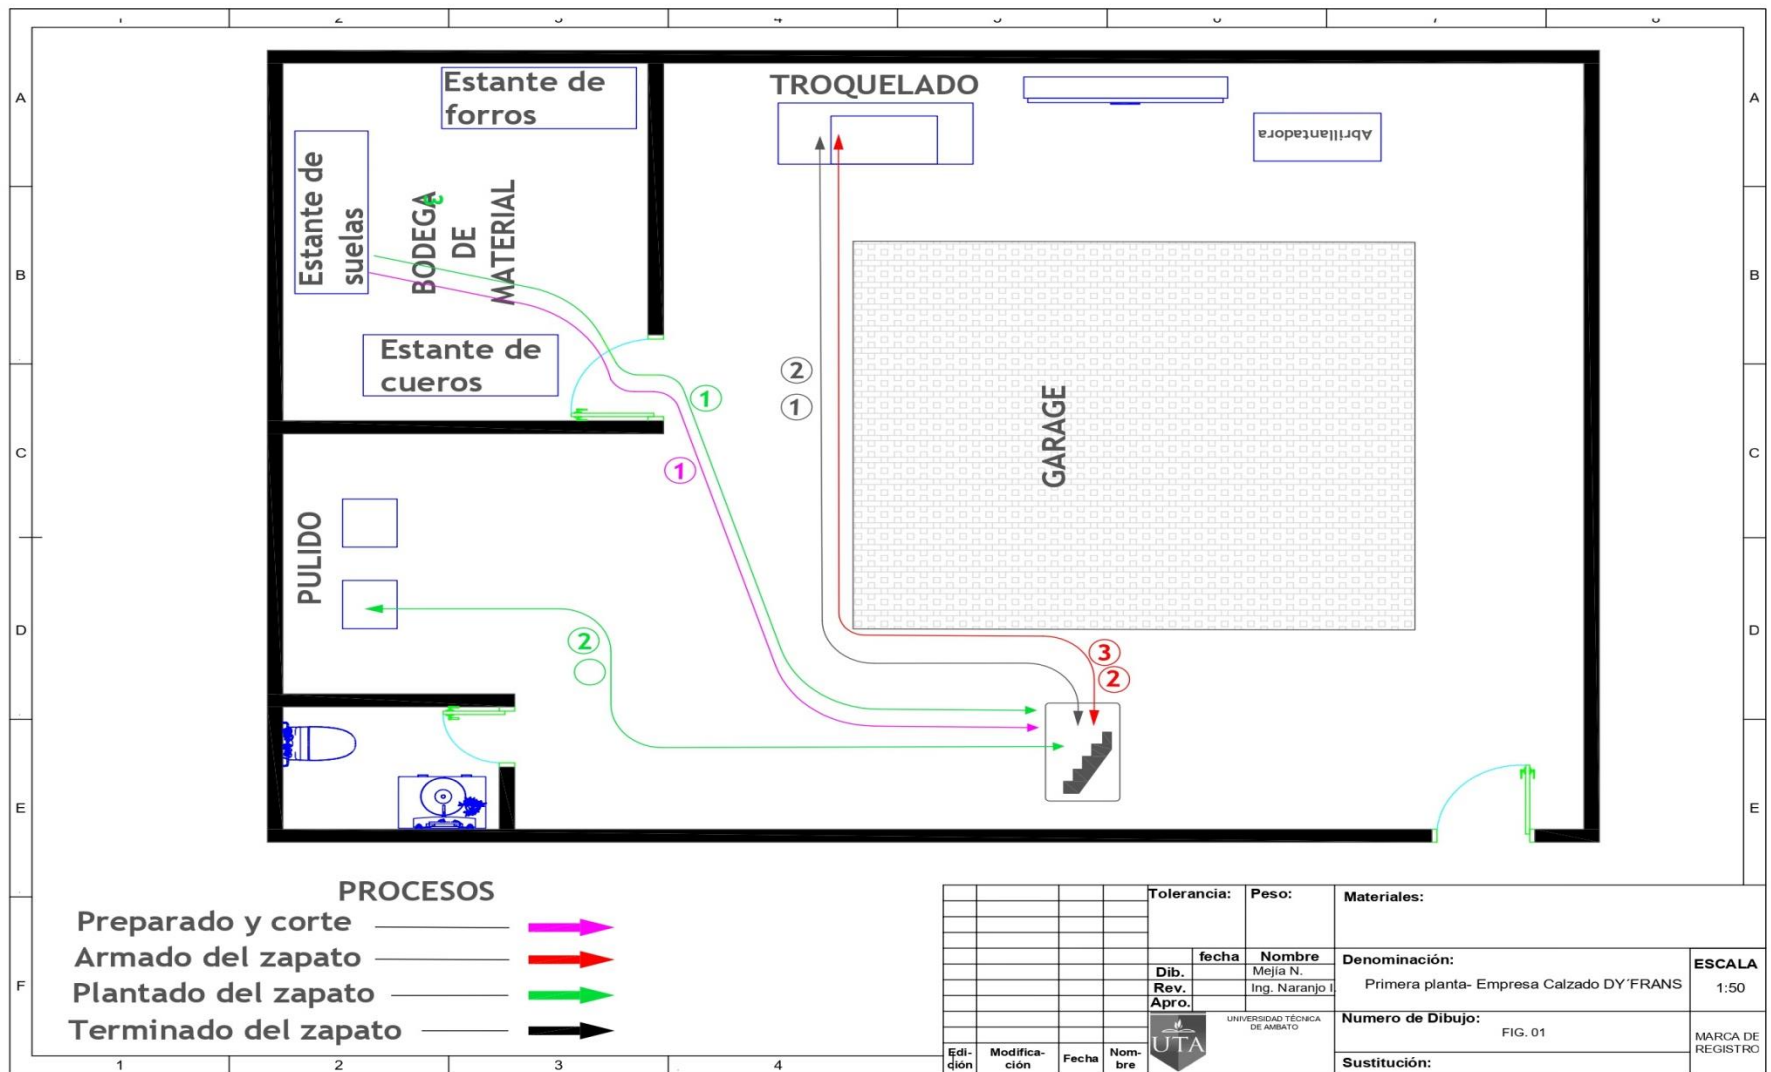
Layout planta baja empresa de calzado Dy'Frans
